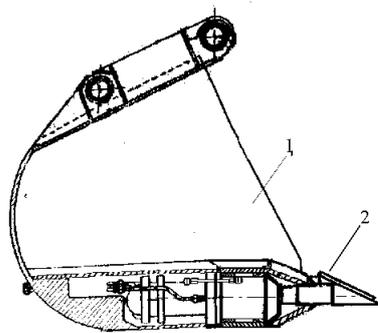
Конструкция ковша активного действия экскаватора экскаватора ЭО-4121 разработки СибАДИ: 1 - корпус ковша; 2 - ударные зубья
